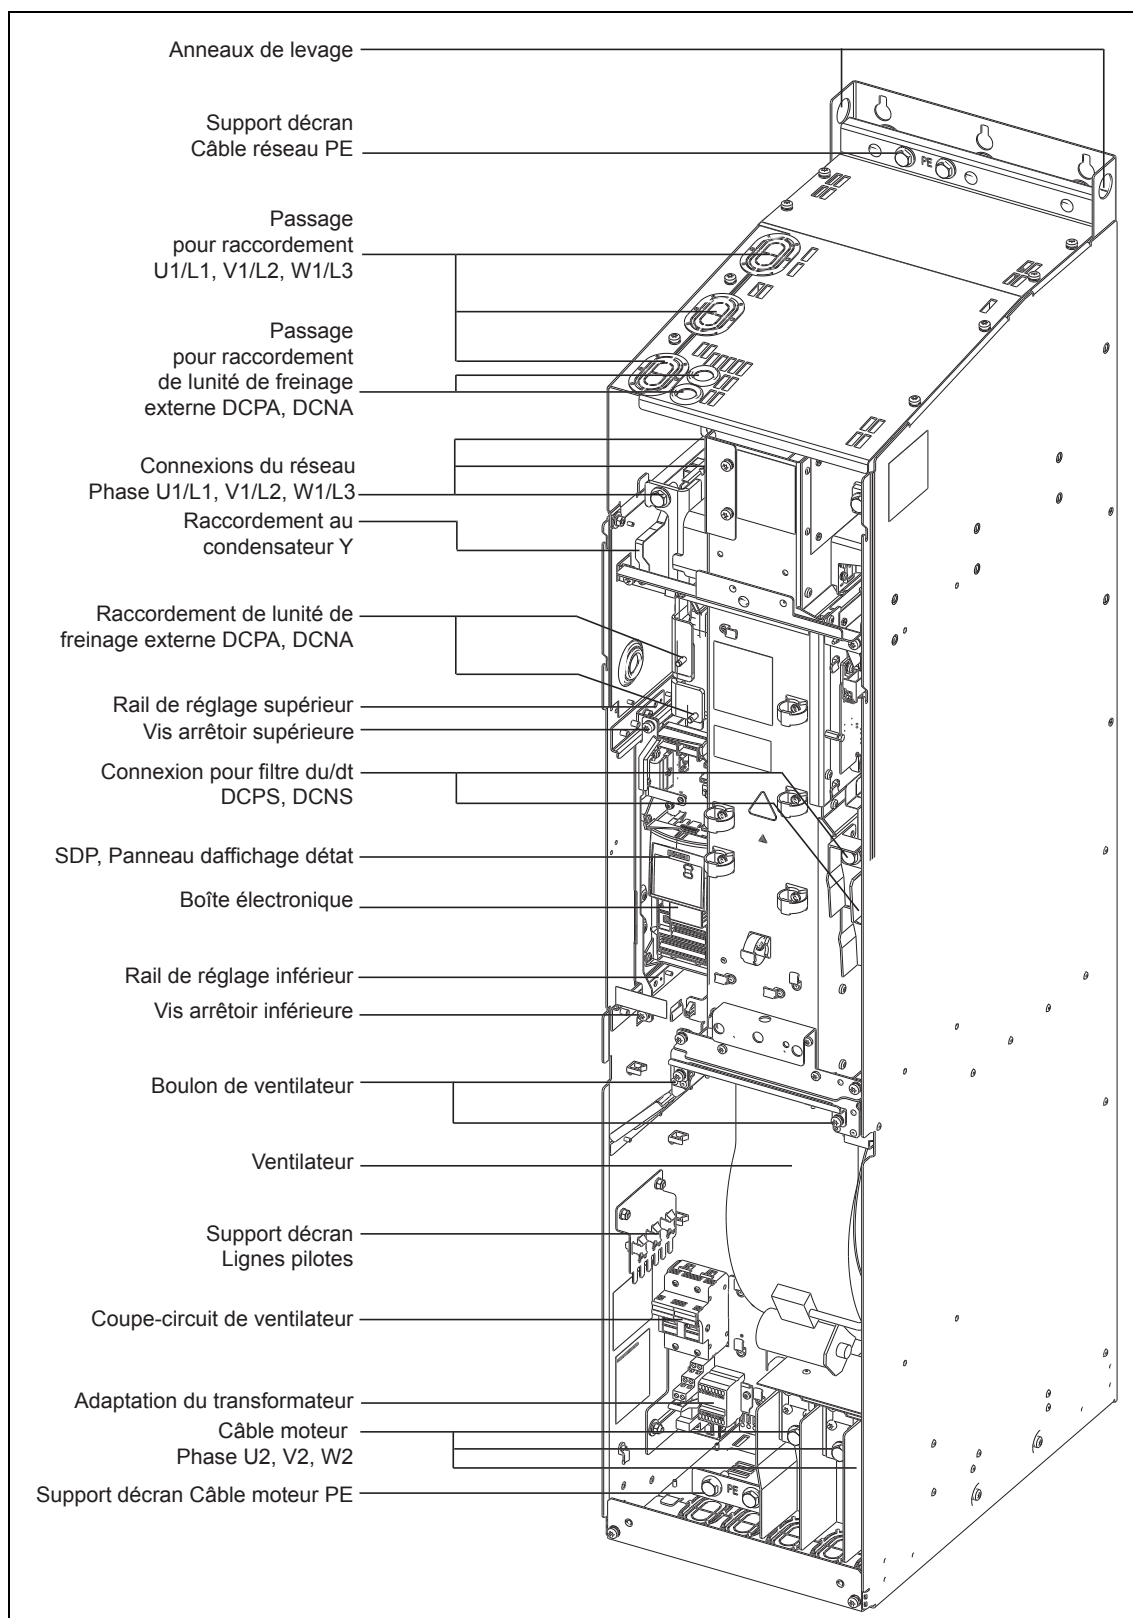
Vue d'ensemble du raccordement, Forme de construction GX
